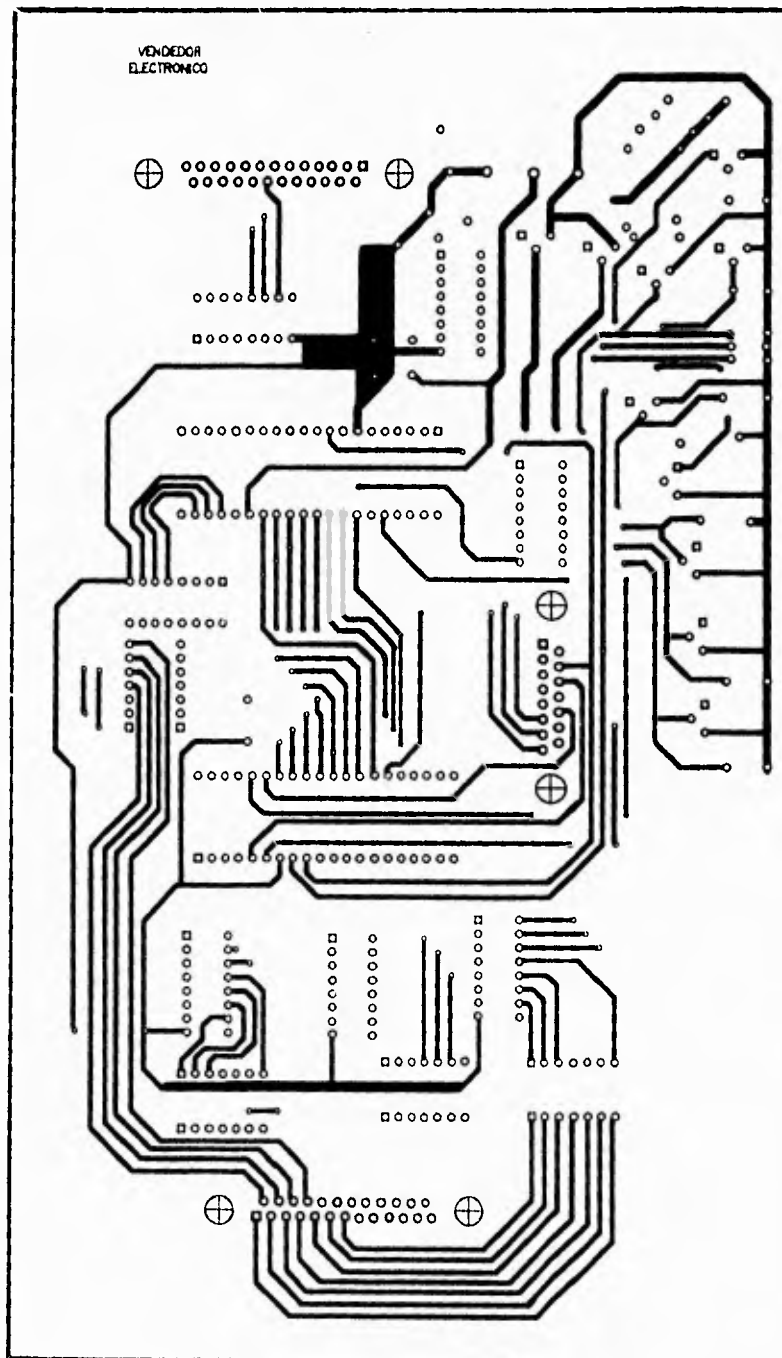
Cara de soldadura del circuito impreso de los driver's de potencia
